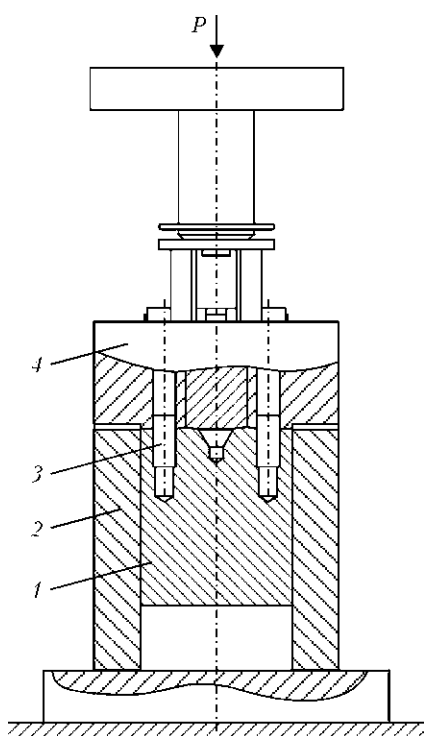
Схема устройства для испытаний шейки оси: 1 — шейка оси; 2 — стакан; 3 — болт; 4 — фиксатор
